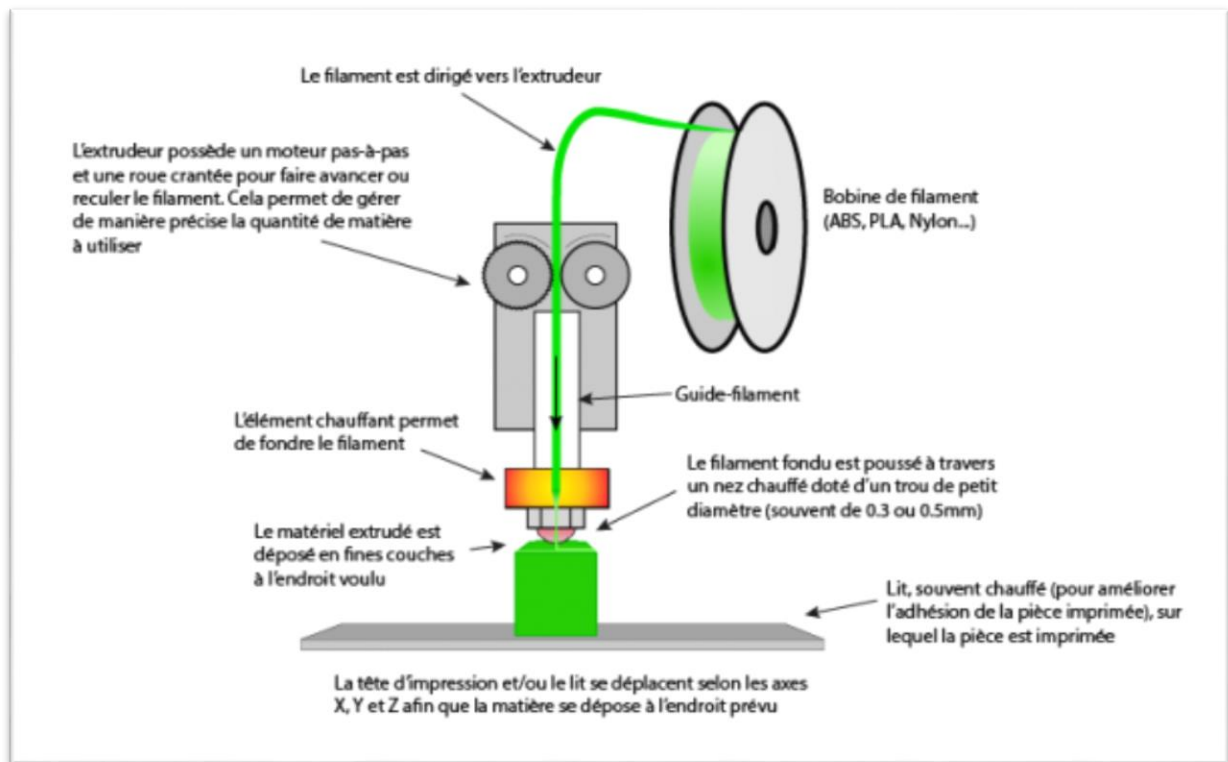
Schéma d'impression dépôt de fil fondu [3]
